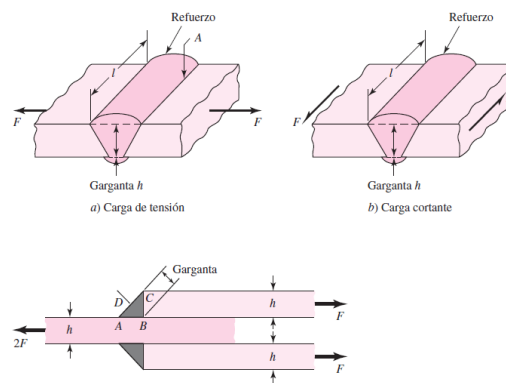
Arriba: Soldadura de tope a tensión y a cortante. Abajo: Soldadura de filete. Fuente:
